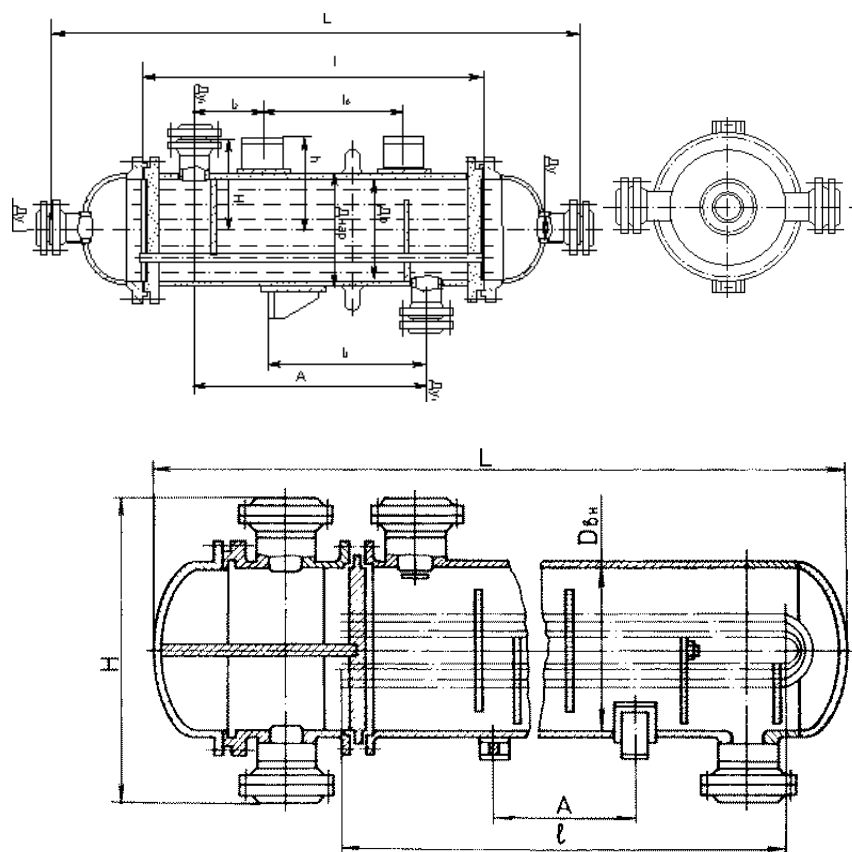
Аппараты кожухотрубчатые с неподвижными трубными решетками одноходовые
